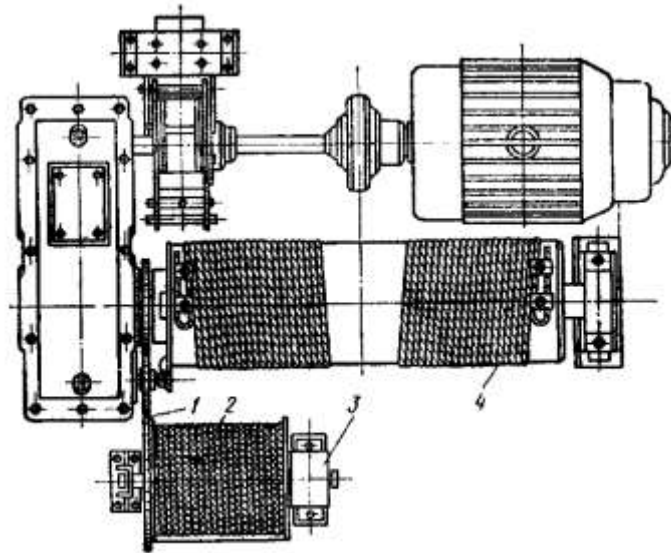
Механизм подъема магнитной крюковой тележки
